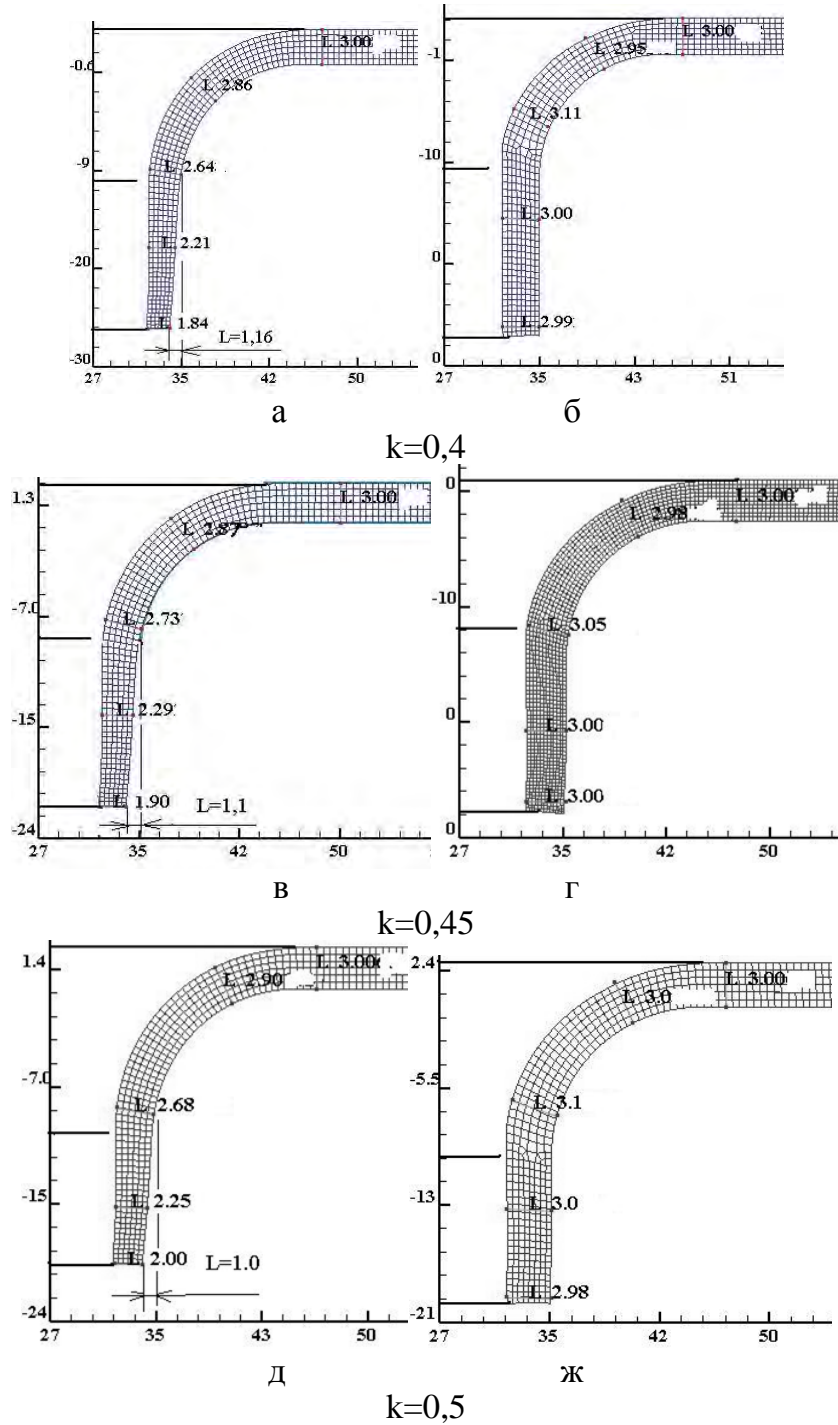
Розміри L (мм) zdeформованих частин заготовок, які отримані відбортуванням традиційної заготовки (а, в, д) та зпрофільованої заготовки (б, г, ж) з коефіцієнтами відбортування 0,4; 0,45; 0,5
